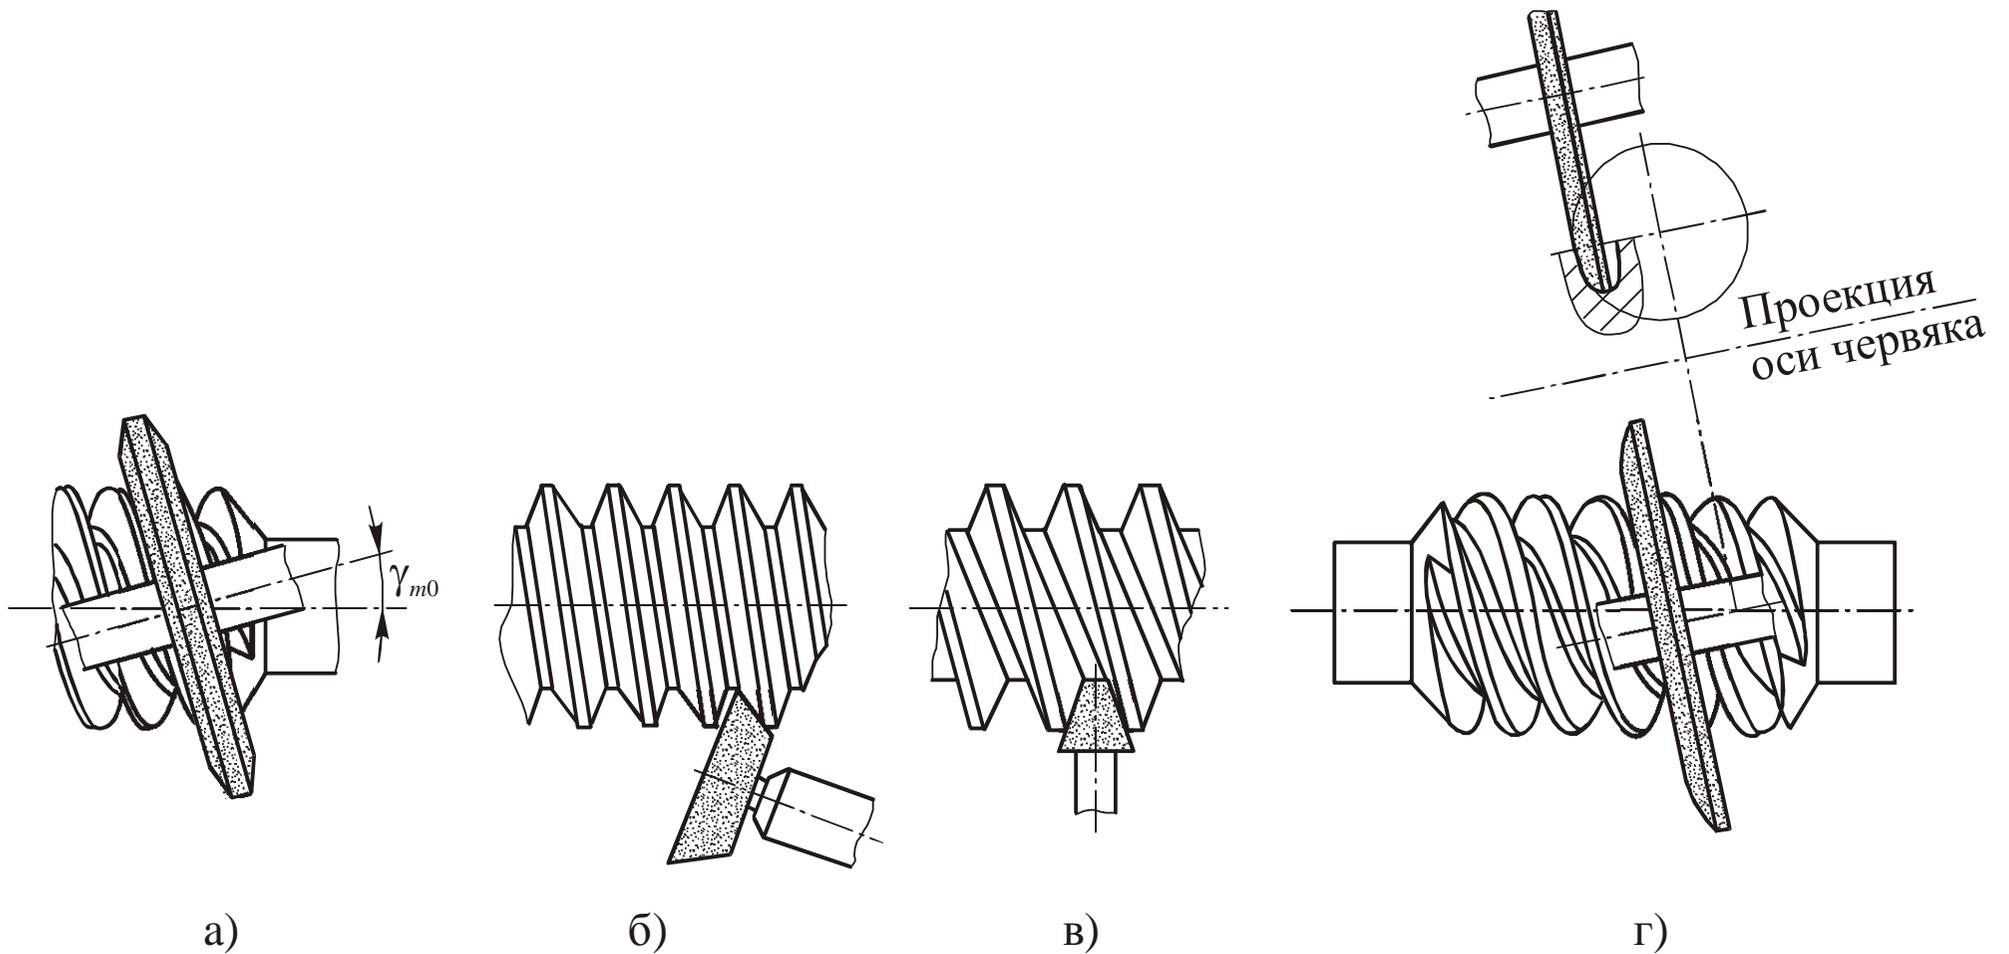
Абразивные круги для шлифования цилиндрических червяков:
